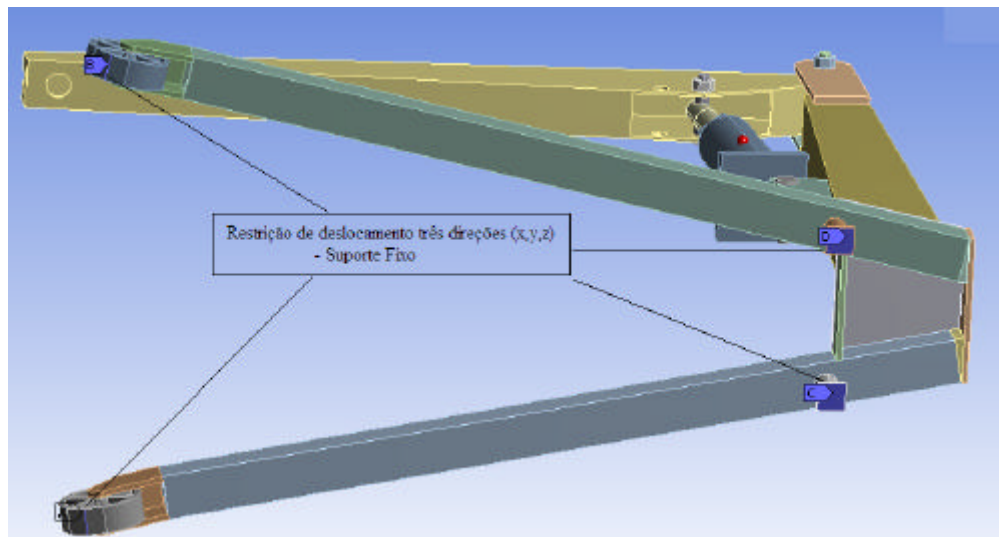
Restrições do Modelo 3D – Vista por debaixo do guincho.
